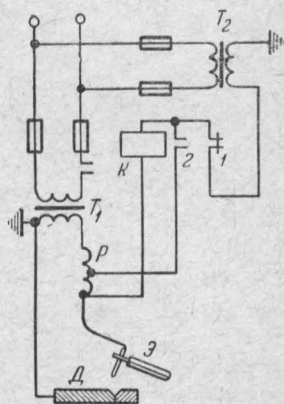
Схема автоматического выключения сварочного трансформатора при разрыве дуги:
